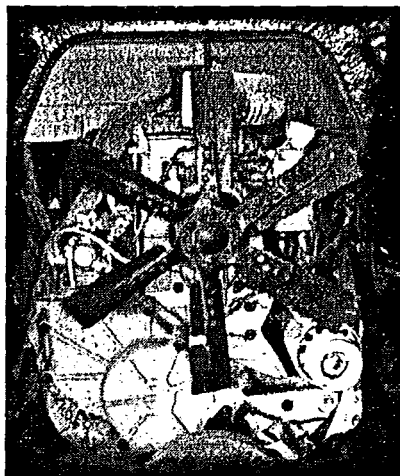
Detalhe frontal do motor diesel que equipa os Fenemês.
